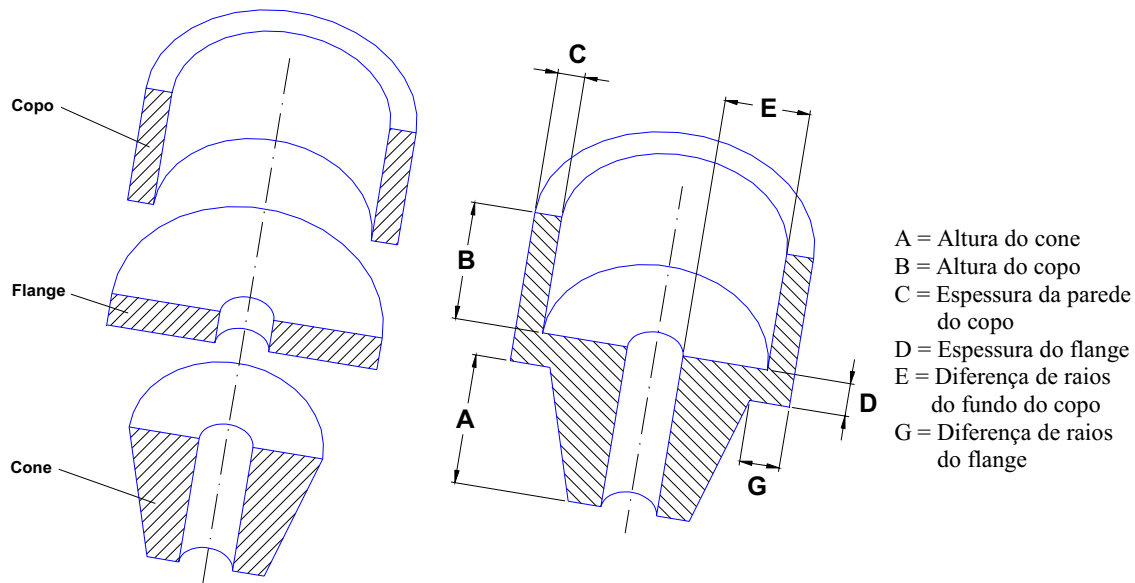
Vista em corte da peça cônica flangeada com as dimensões de referência.
